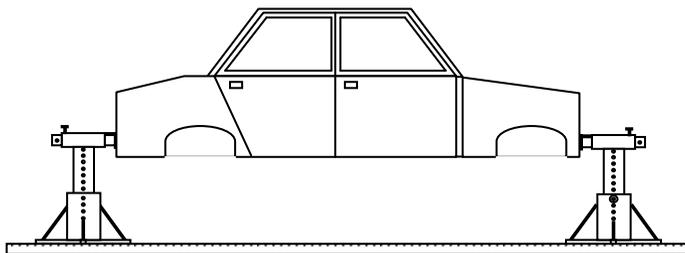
Расположение несущего кузова автомобиля в кантователе
